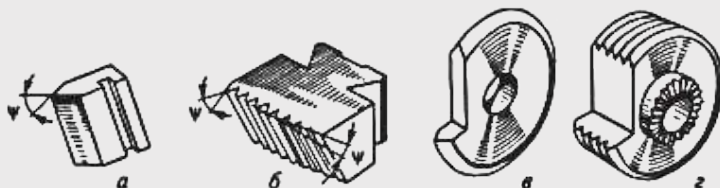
Типи різбових фасонних різців: а — різець призматичний односторонній; б — різець призматичний багатонитковий (гребінка); в — різець круглий односторонній; г — різець круглий багатонитковий (гребінка)
